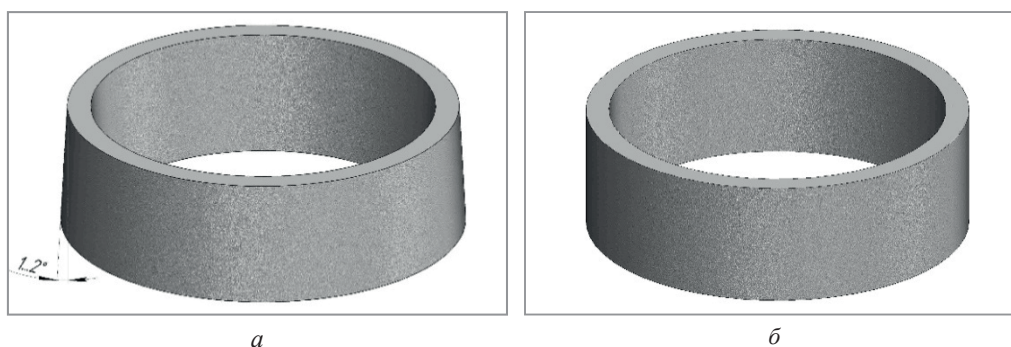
Маслотные заготовки поршневых колец высотой 32–40 мм: *а* – традиционная отливка маслотной заготовки для производства поршневых колец с уклонами; *б* – отливка «маслота» без литейных уклонов
